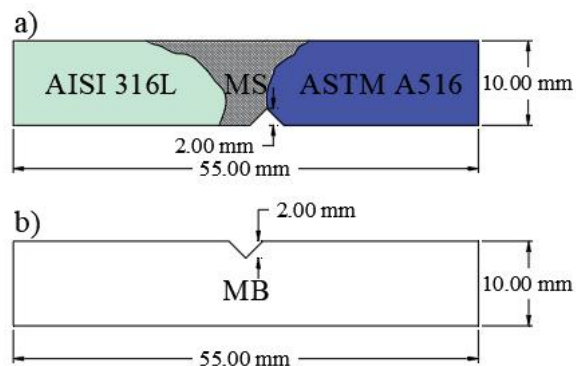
Esquema representativo de las muescas en las probetas para ensayo de impacto Charpy; a) unión soldada y b) metales base.
